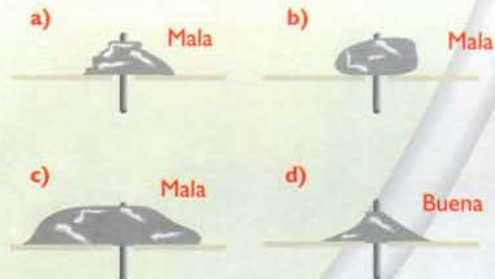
Aspecto de una buena soldadura y varias mal hechas
